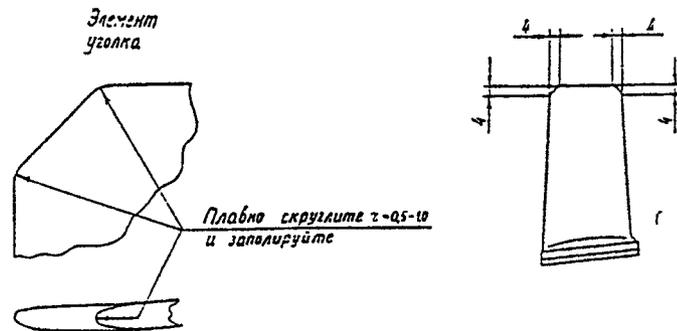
Обрезка уголков лопаток 1-й ступени компрессора
